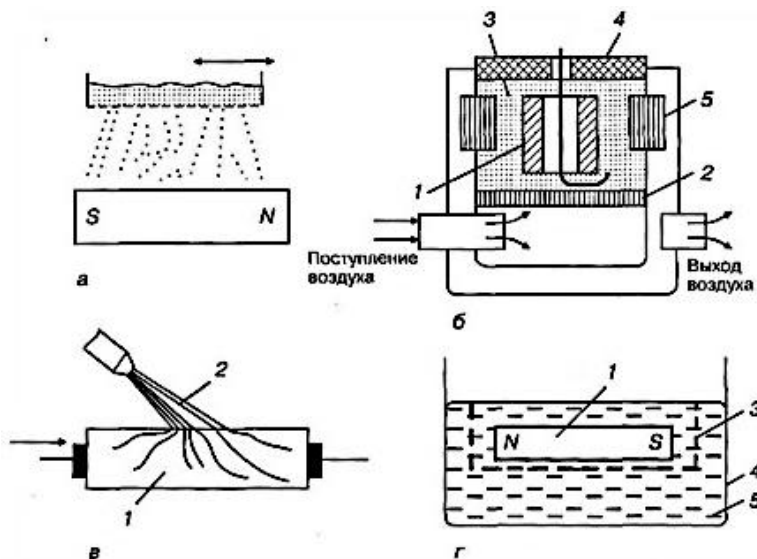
Способы нанесения магнитопорошкового индикатора [9]
